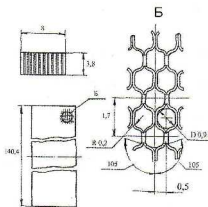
Конструкция активной поверхности сотовой уплотнения.
